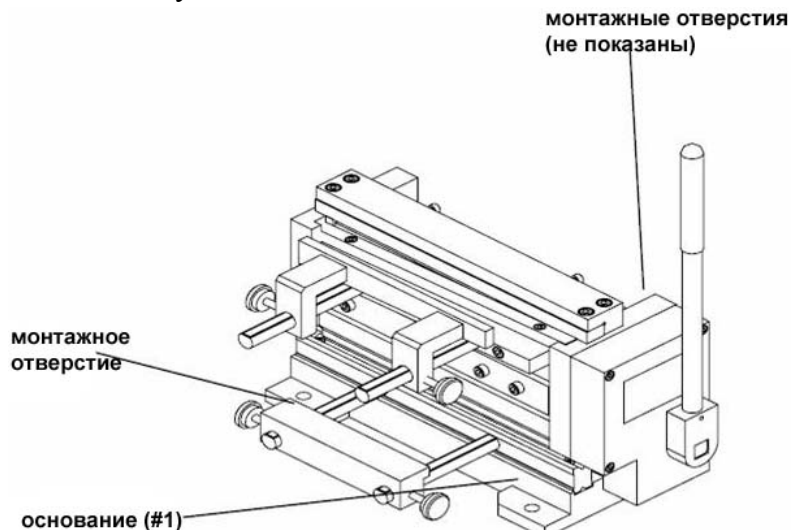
Установка станка для резки/гибки на деревянный верстак
